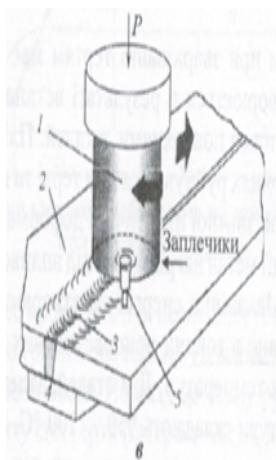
Схема процесу зварювання тертям з перемішуванням:
